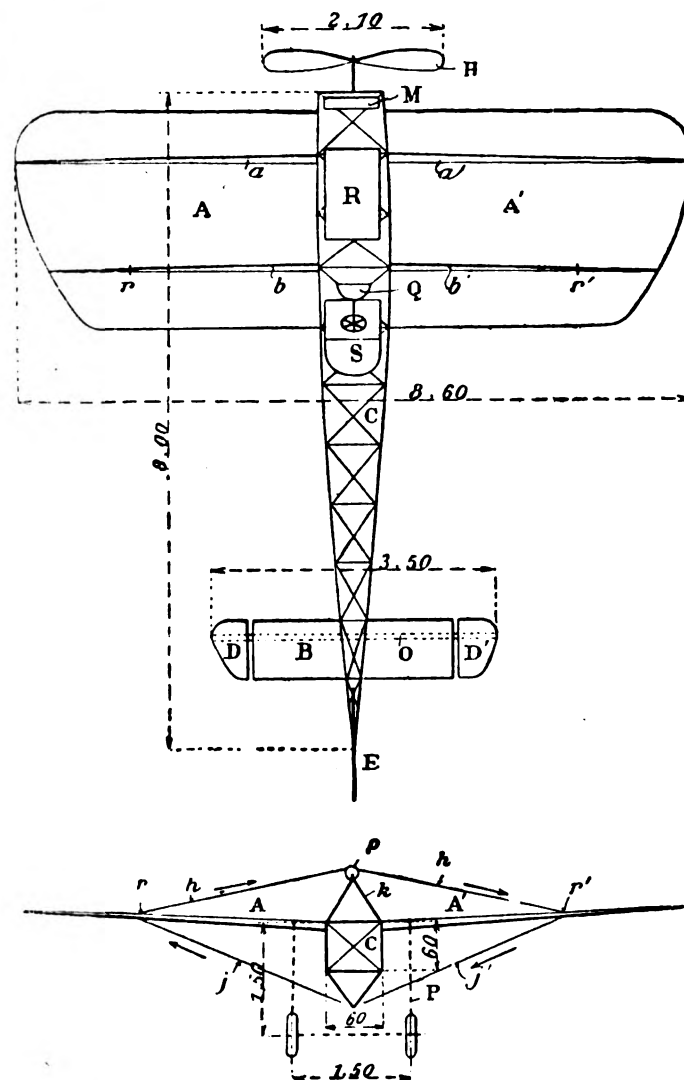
Monoplano Blériot, tipo 1910. - Pianta e sezione.
